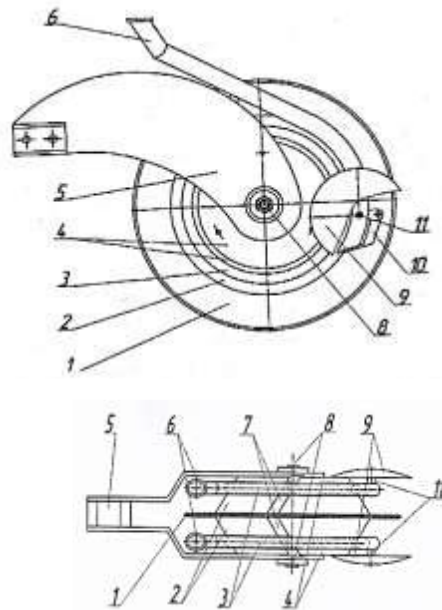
Комбінований однодисковий сошник з двосторонніми ребордами та сферичними дисковими загортачами для вузькорядного посіву: а – вид збоку; б – вид зверху; 1 – плоский диск; 2, 4 – реборди; 3 – борозноутворювачі; 5 – корпус; 6 – насіннепроводи; 7 – чистики; 8 – вісь; 9 – сферичні диски; 10 – клапан; 11 – осі.
